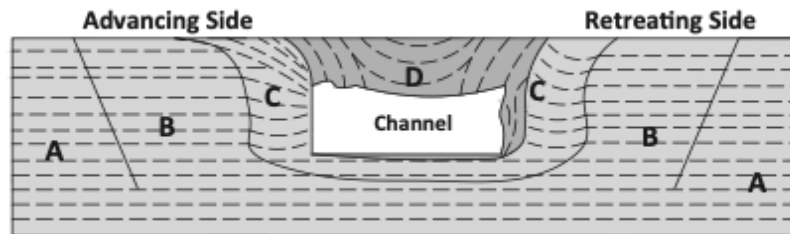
Representação esquemática da secção transversal de um canal produzido pela variante FSC *without shoulder-workpiece clearance* [17].
